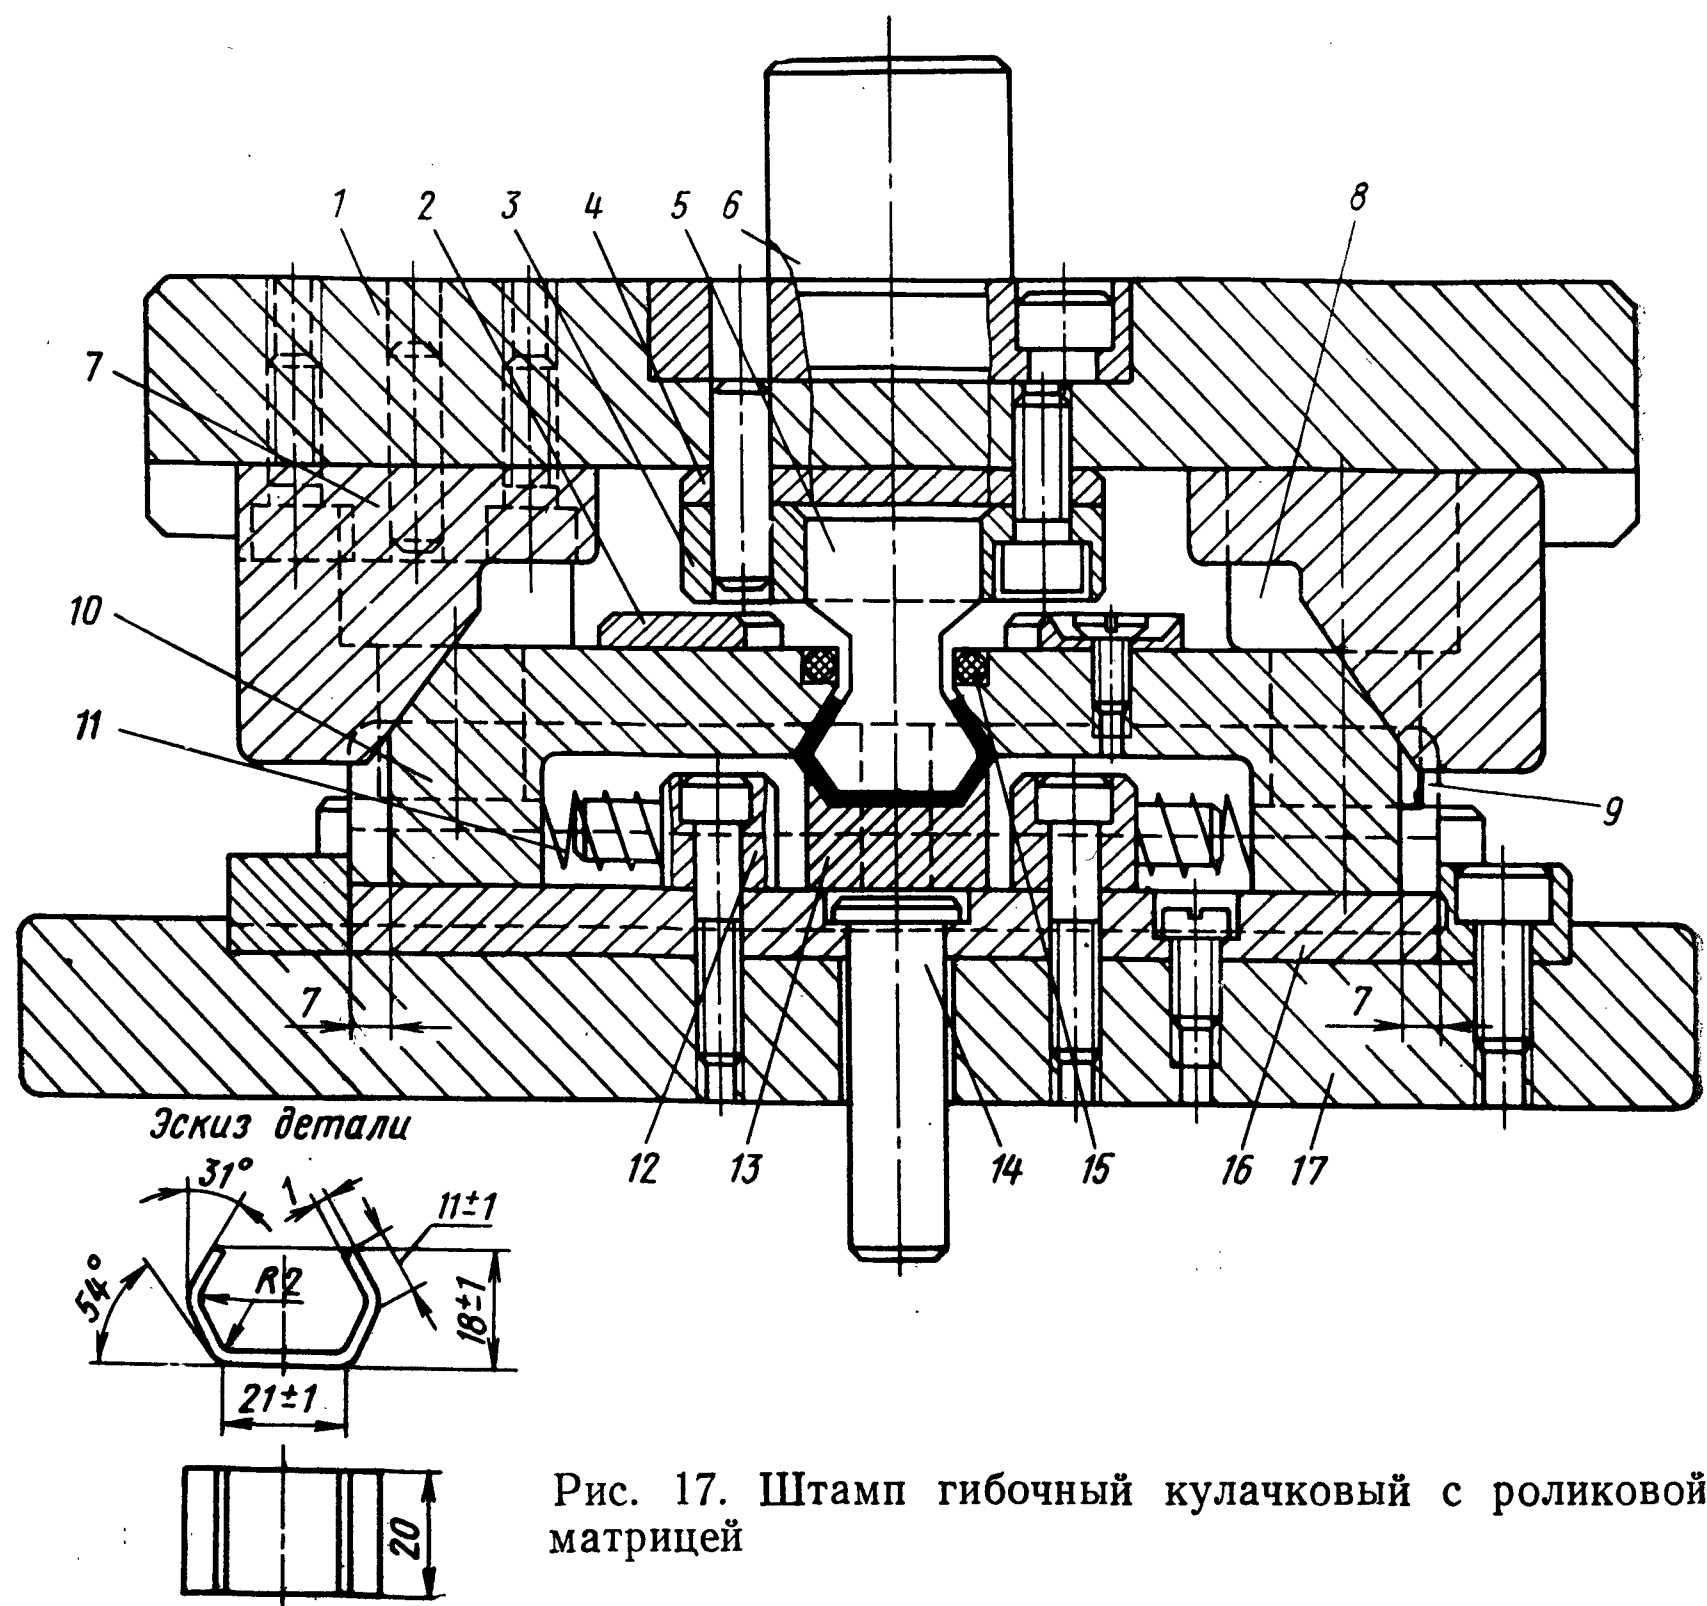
Штамп гибочный кулачковый с роликовой матрицей
